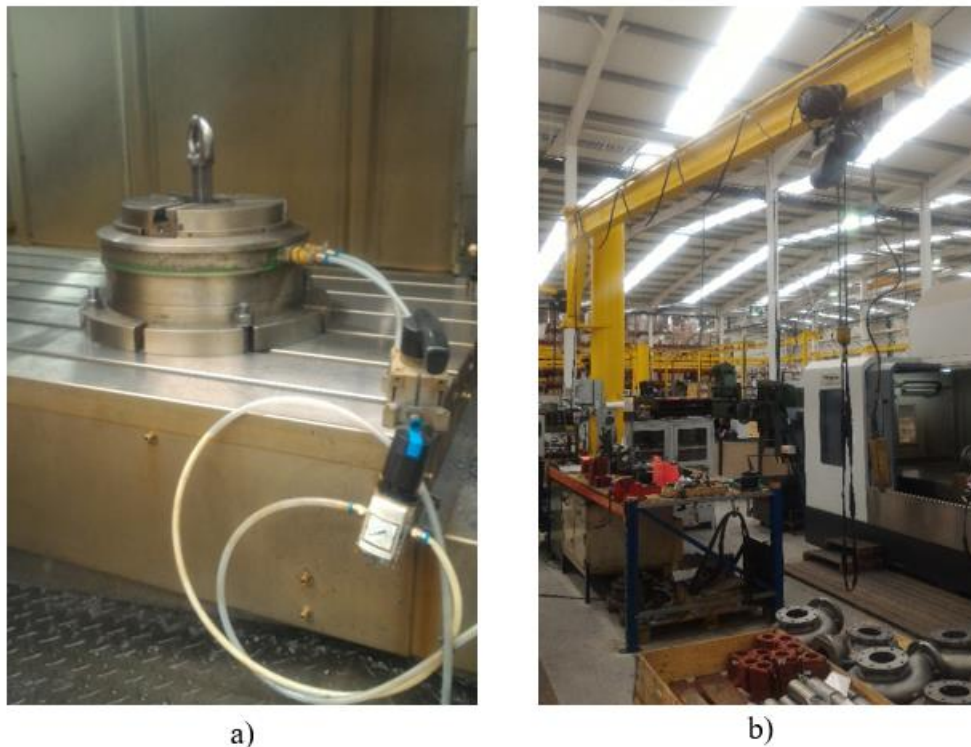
Sistemas auxiliares de maquinagem: a) Bucha pneumática; b) Guindaste.
